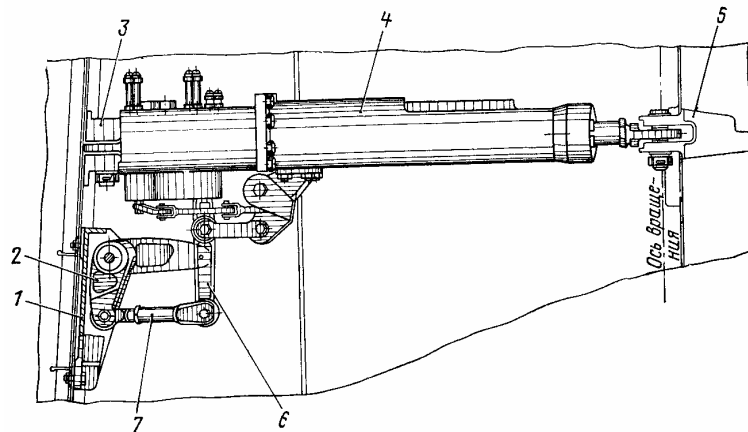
Установка рулевого привода РП-56 руля направления: 1 3, 5—кронштейн; 2—двулучевая качалка; 4—рулевой привод РП-56; 6—входной рычаг рулевого привода РП-56; 7—тяга
